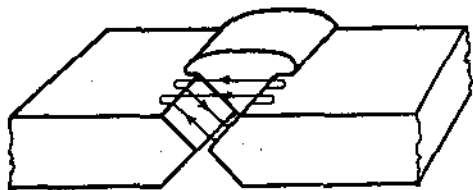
Правильный образец X-образного сварного соединения. Обратите внимание на направление электродов при наплавлении смежных слоев.
